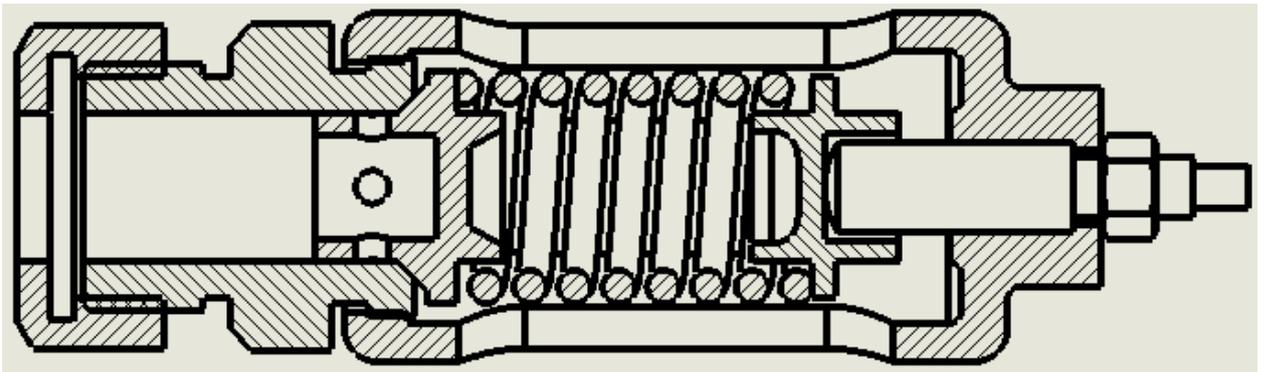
Изменение угла штриховки для деталей Седло и опора
